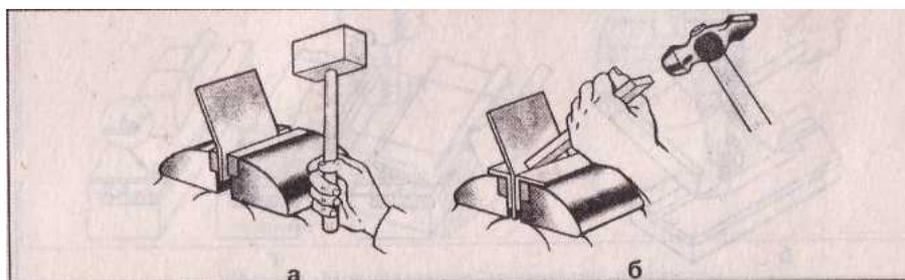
Сгибание заготовок из тонколистового металла в тисках:
